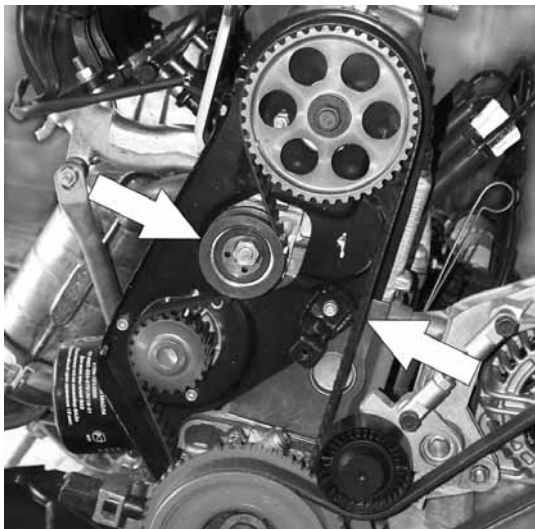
Проверка натяжения ремня привода ГРМ 8-клапанного двигателя
